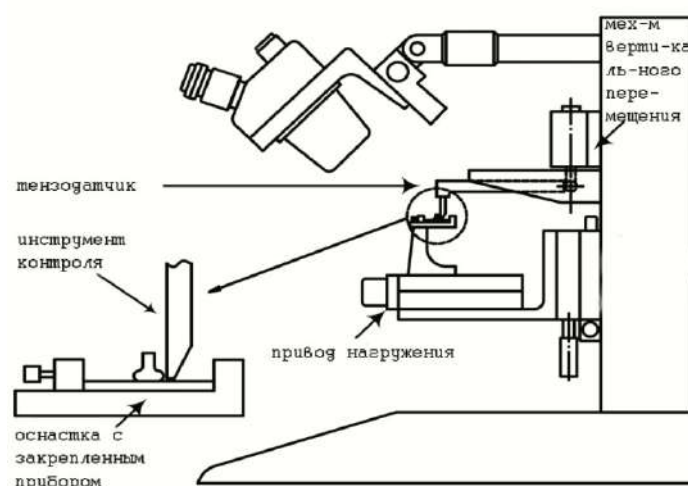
Схема испытания сварного соединения на сдвиг.
